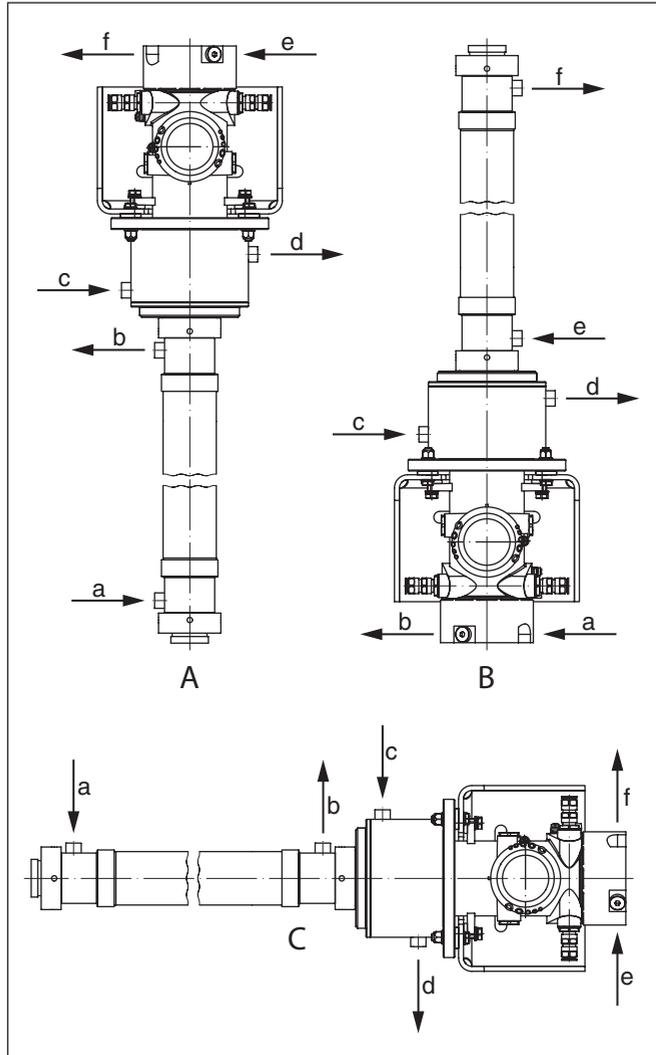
Posizione di montaggio del sistema di raffreddamento - prestare attenzione alla direzione di scorrimento del refrigerante (a, b, c ...)
